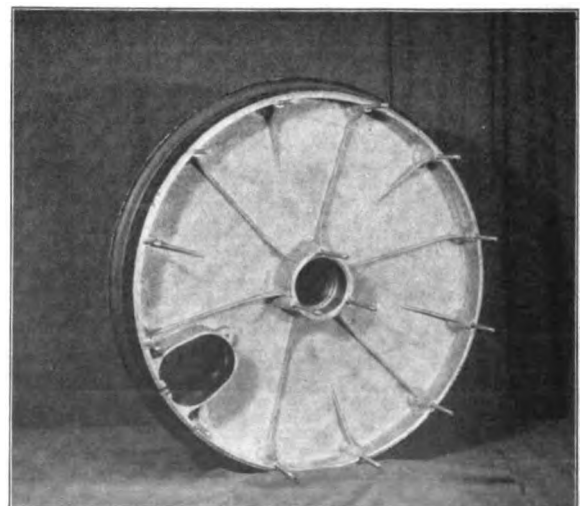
Innenansicht einer Hälfte eines Elektron-Flugzeuganlaufrades.
